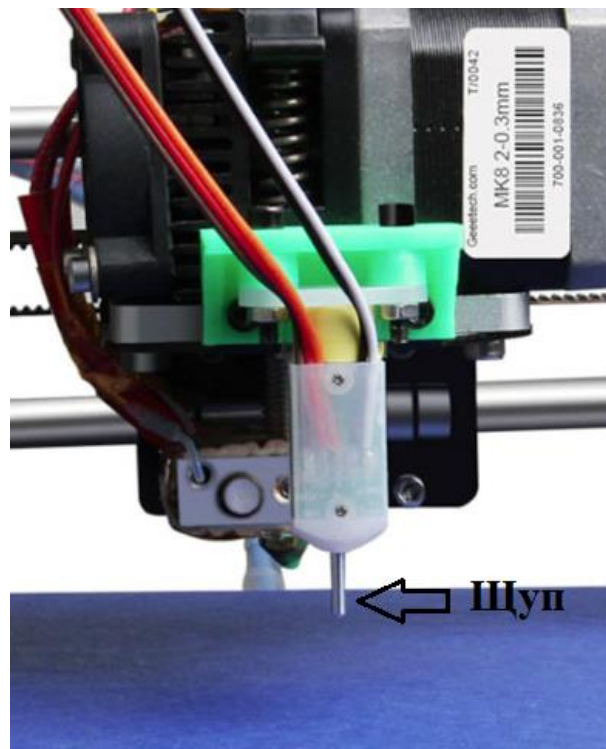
Механічний замір щупом до поверхні платформи 3D принтера
